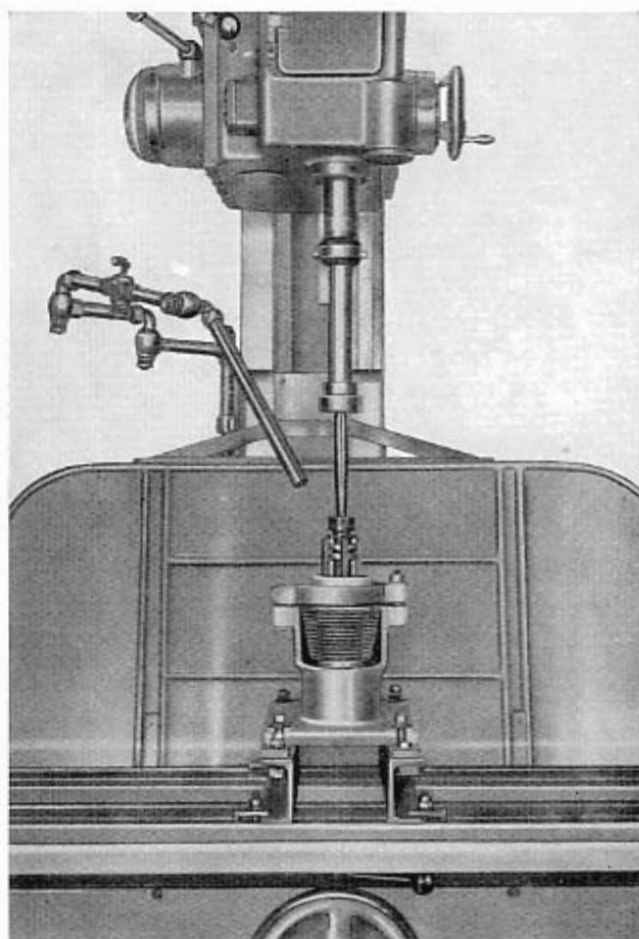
Rodage sur machine fixe d'un cylindre monté sur l'outil A. 60000, au moyen du rodoir A. 11209.
